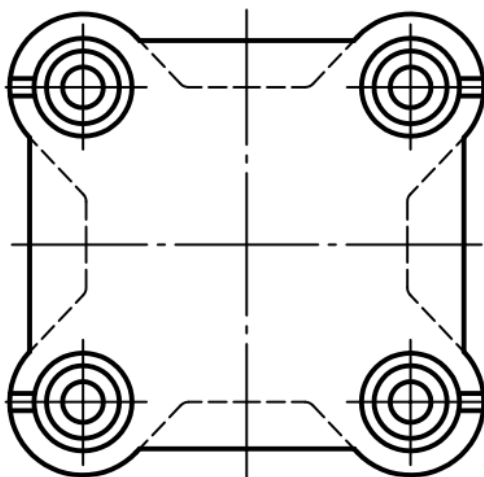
Загальний вигляд блока штамп з чотирма напрямними вузлами
